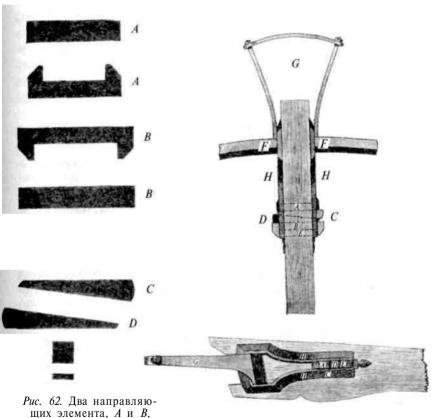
Два направляющих элемента, А и В, и два клина, С и D, используемые для подтягивания накладок из сварочной стали, которые прикрепляют лук к ложу
